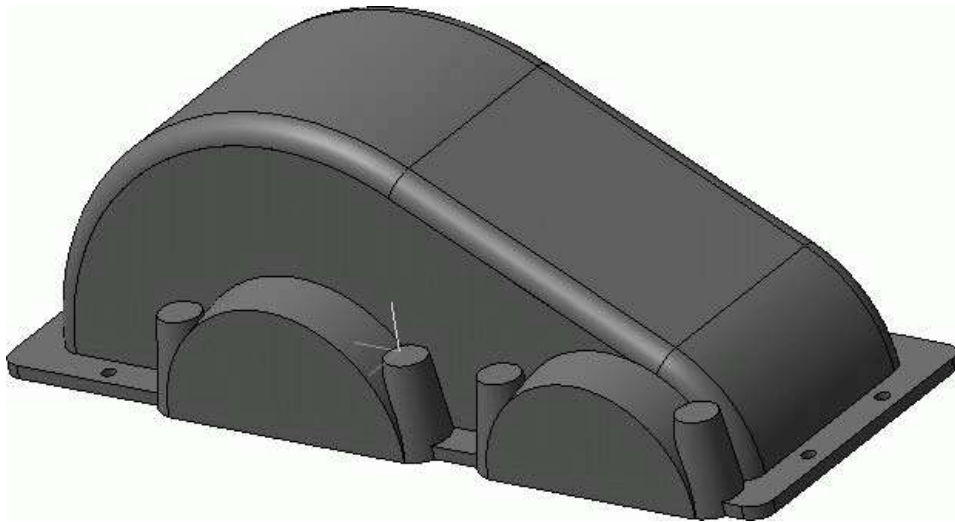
Добавление мест крепления крышек подшипников и бобышек в модель крышки редуктора
